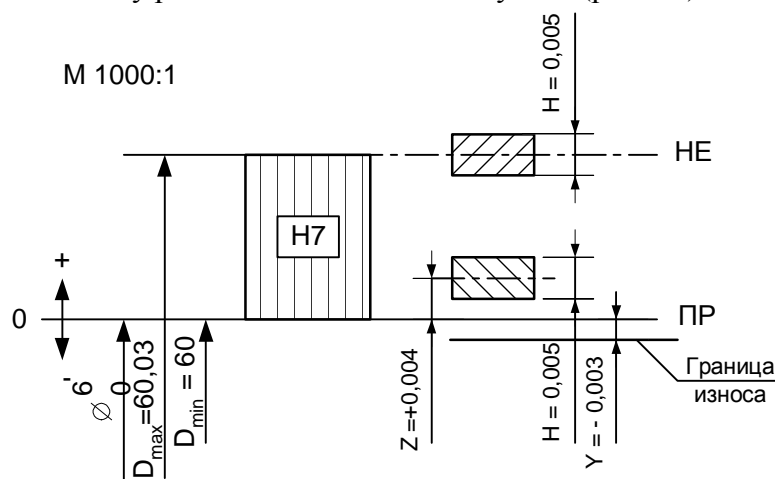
Схема расположения полей допусков калибра-пробки
